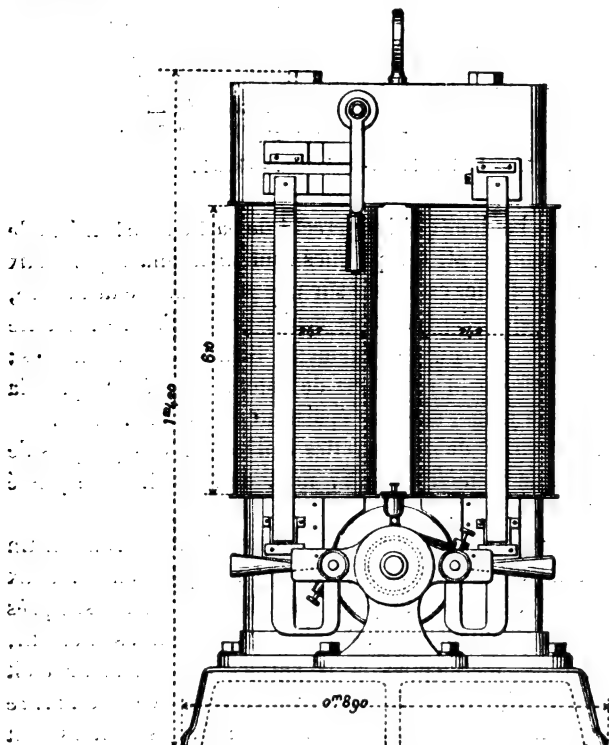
Machine Edison-Hopkinson. — Vue en bout.
